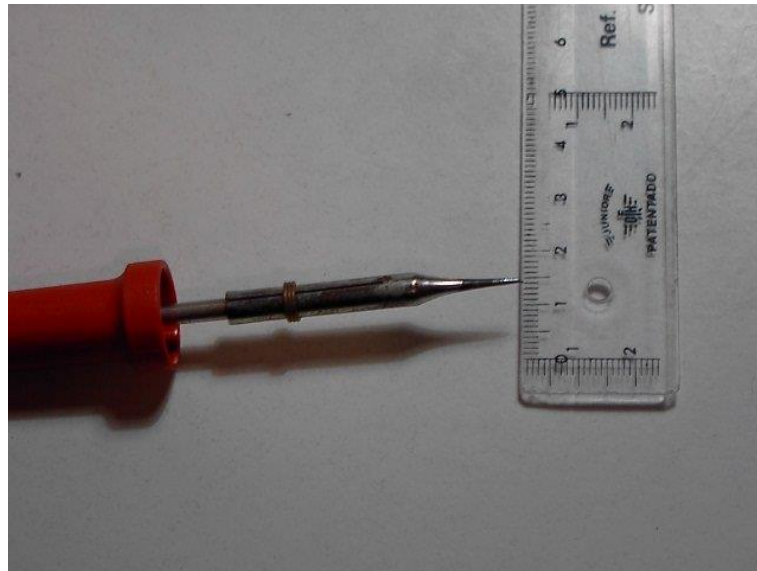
SOLDADOR DE PUNTA FINAS
